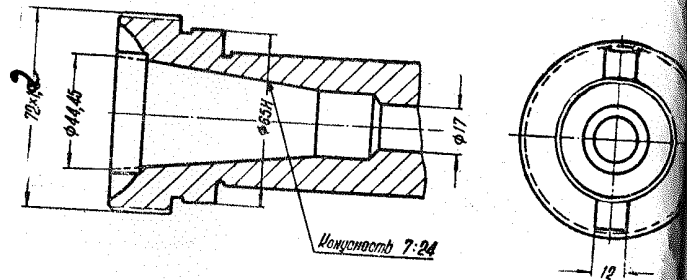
а. Эскиз конца шпинделя поворотной головки станка модели 6М83Ш
